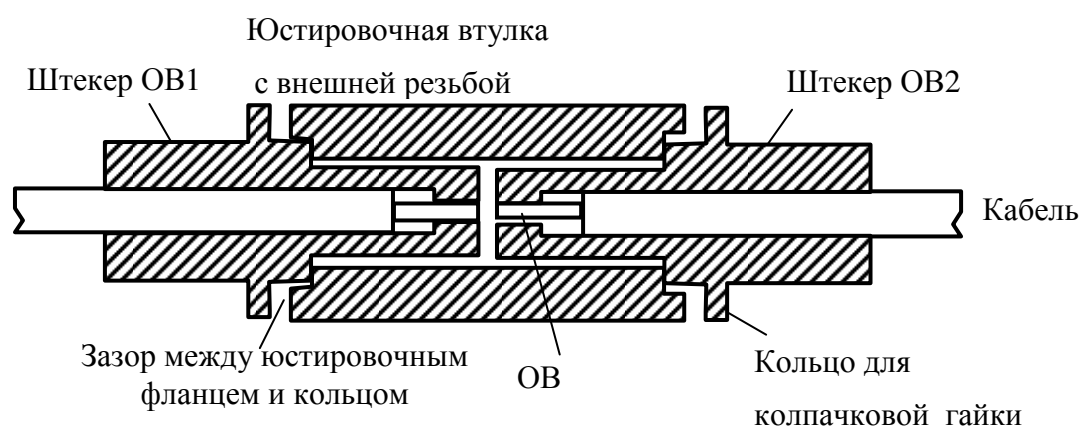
Разрез конструкции соединителя с прямой втулкой
